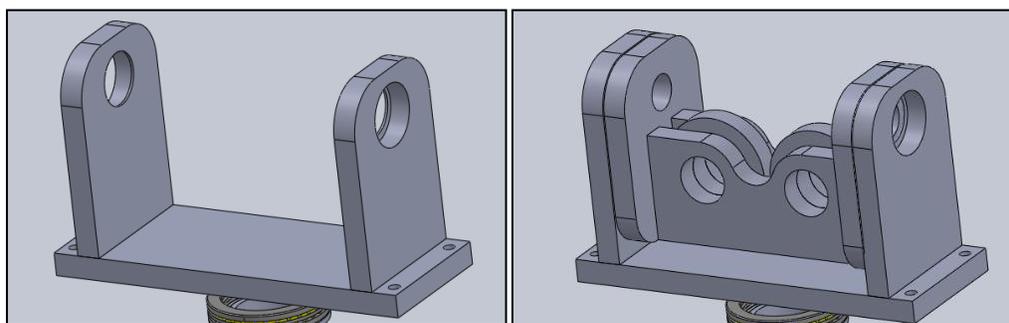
Pilares de sujeción y caja de soporte (Pieza N° 11 de ensamble). Fuente: Elaboración propia.
